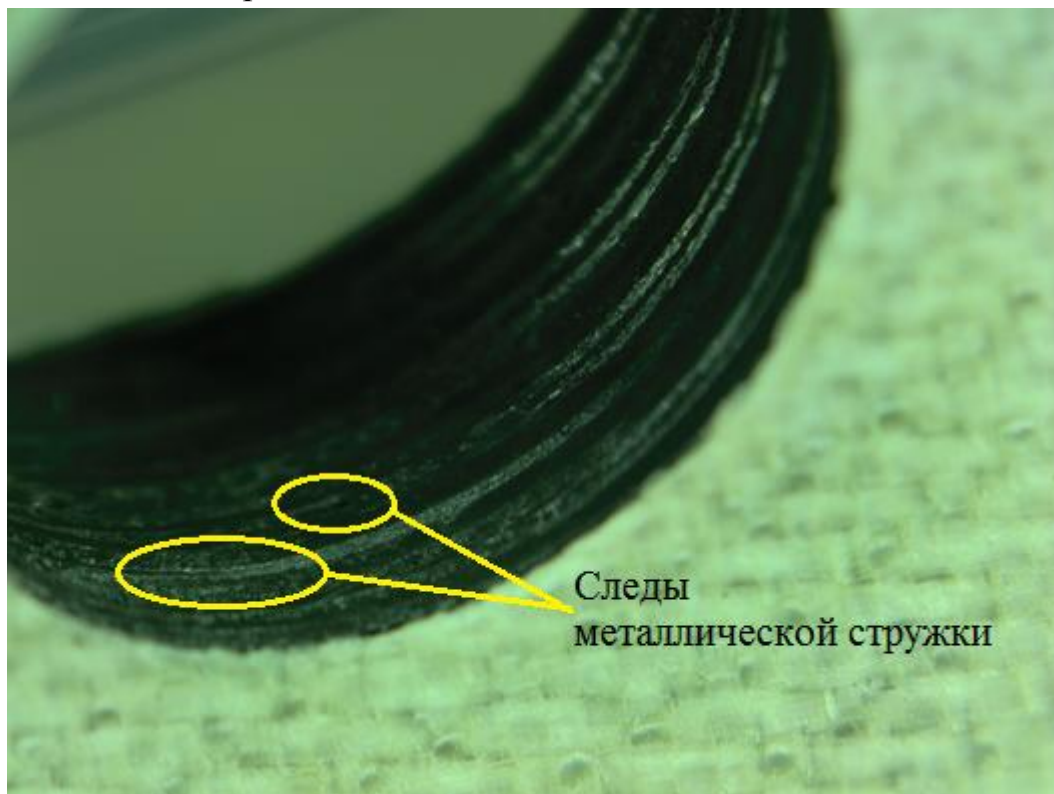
Повреждения на обработанной кромке пластины из ПКМ при сверлении пакета металл-композит-металл, при повышенных оборотах
